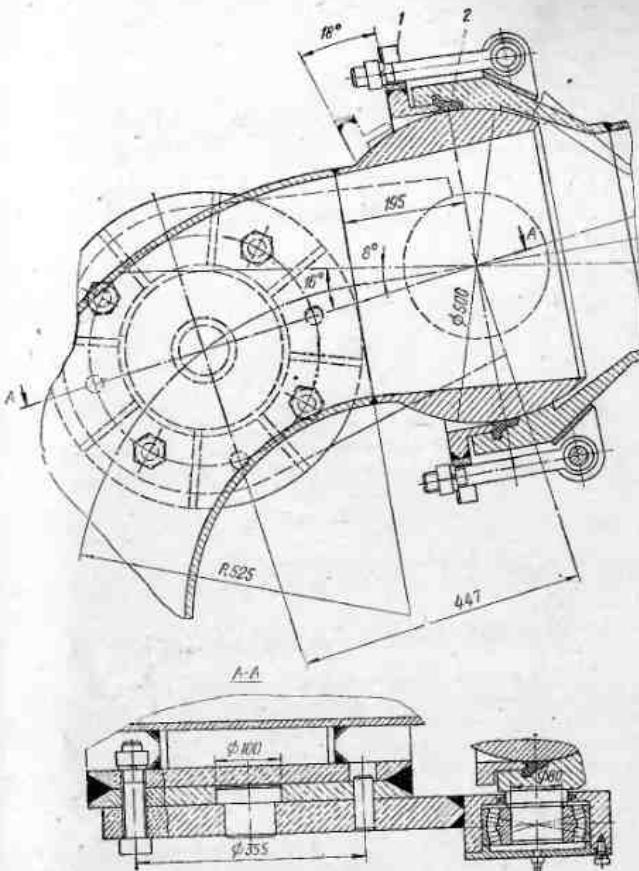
Конструкция шарового шарнира гидромонитора ГМ-350 (175-150)
